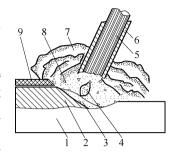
电弧焊接过程 1-焊件 2-焊缝 3-熔池 4-金属熔滴 5-焊芯 6-焊条药皮 7-气体 8-液态熔渣 9-固态渣壳
